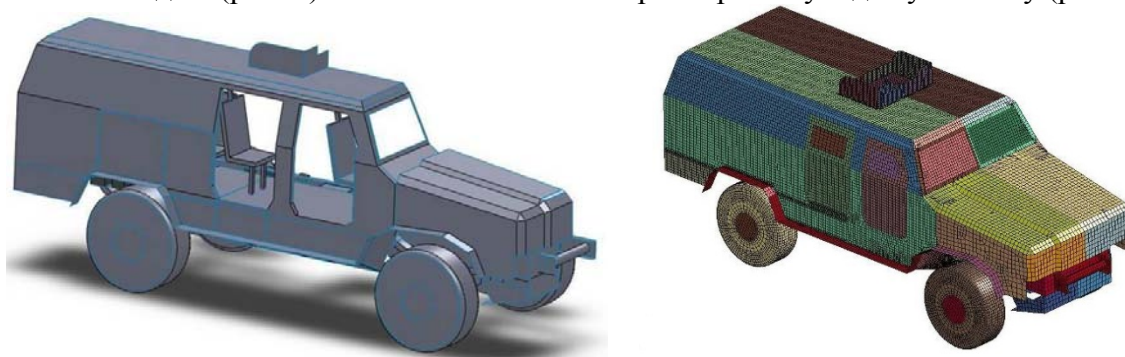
Геометрична модель корпусу СБА Козак-001 та загальний вигляд SE-моделі зразка
